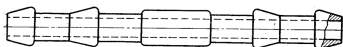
Двухсторонний ниппель для соединения шлангов
